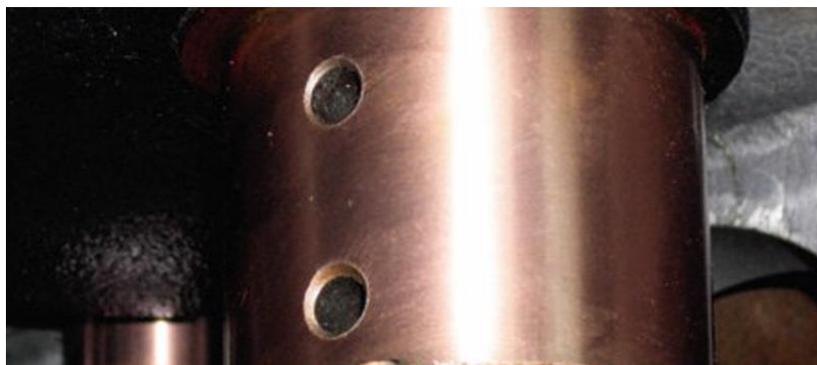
Поверхность шейки коленчатого вала после ФАБО
